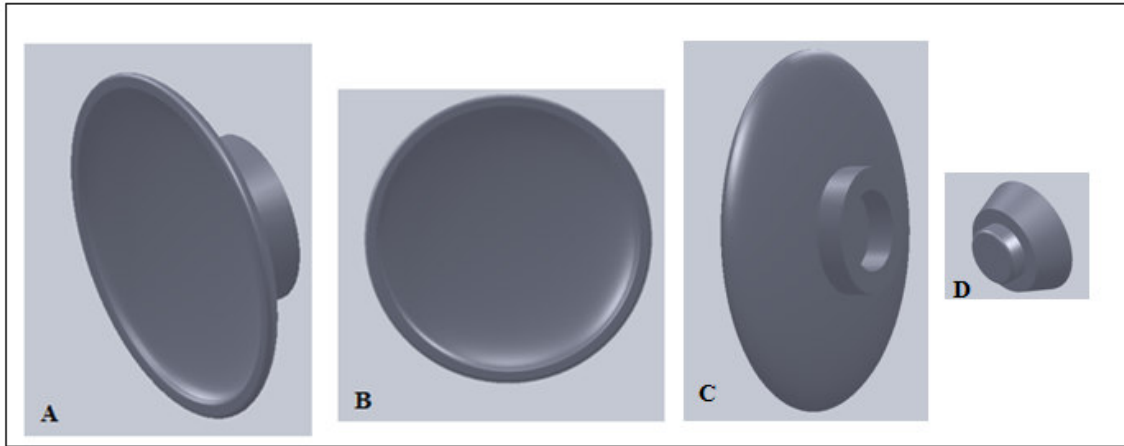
Aplicador (A) - vista anterior do prato aplicador (B) vista posterior do prato aplicador (C) e pino aplicador (D)
